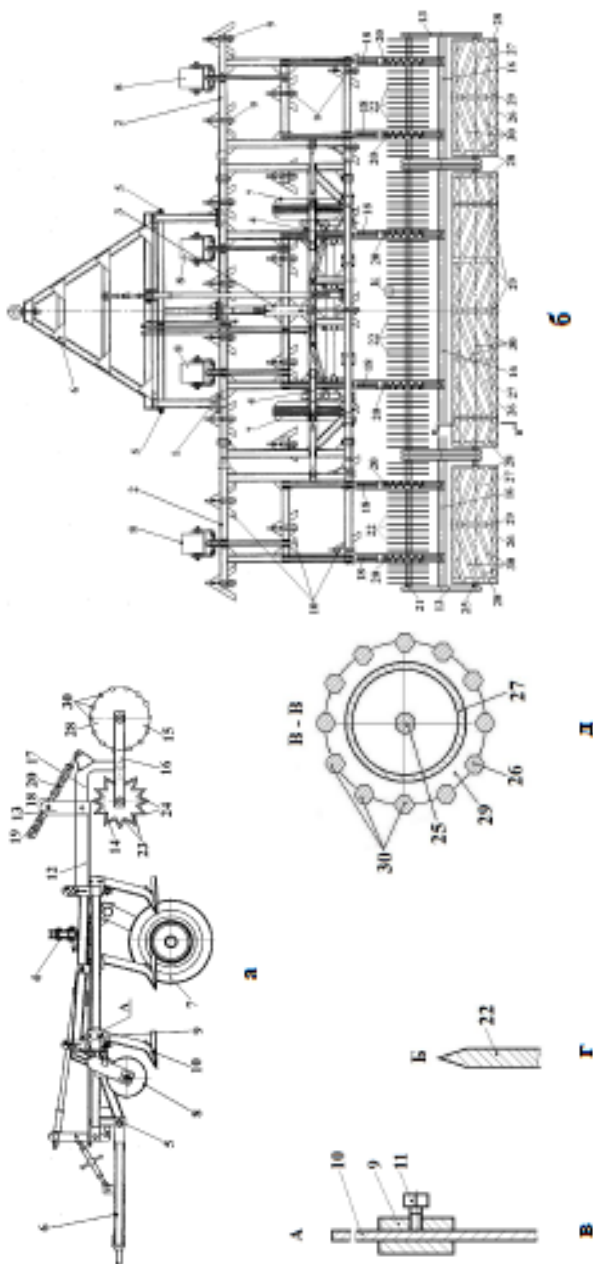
Агрегат для поверхностной обработки почвы (обозначения в тексте): а – вид сбоку, б – вид сверху, в – сечение держателя рабочего органа, г – поперечное сечение заточенной вершины дискового рыхлителя, д – поперечное сечение катка выравнивающего типа; 1, 2 – центральная и боковая секции рамы соответственно; 3, 4 – механизм перевода; 5 – палец; 6 – снап; 7, 8 – транспортные и опорные колеса соответственно; 9 – держатель; 10 – рабочие органы; 11 – болт; 12 – балка; 13 – катковые приставки; 14, 15 – каток рыхлительного и выравнивающего типа соответственно; 16 – H-образная рама; 17 – кронштейн; 18 – штанга; 19 – гайка; 20 – пружина; 21 – ось; 22 – Дисковые рыхлители; 23 – треугольные выемки; 24 – заточенная вершина; 25 – ось; 26, 27 – наружный и внутренний барабаны; 28, 29 – боковые и промежуточные Диски соответственно; 30 – пружок
